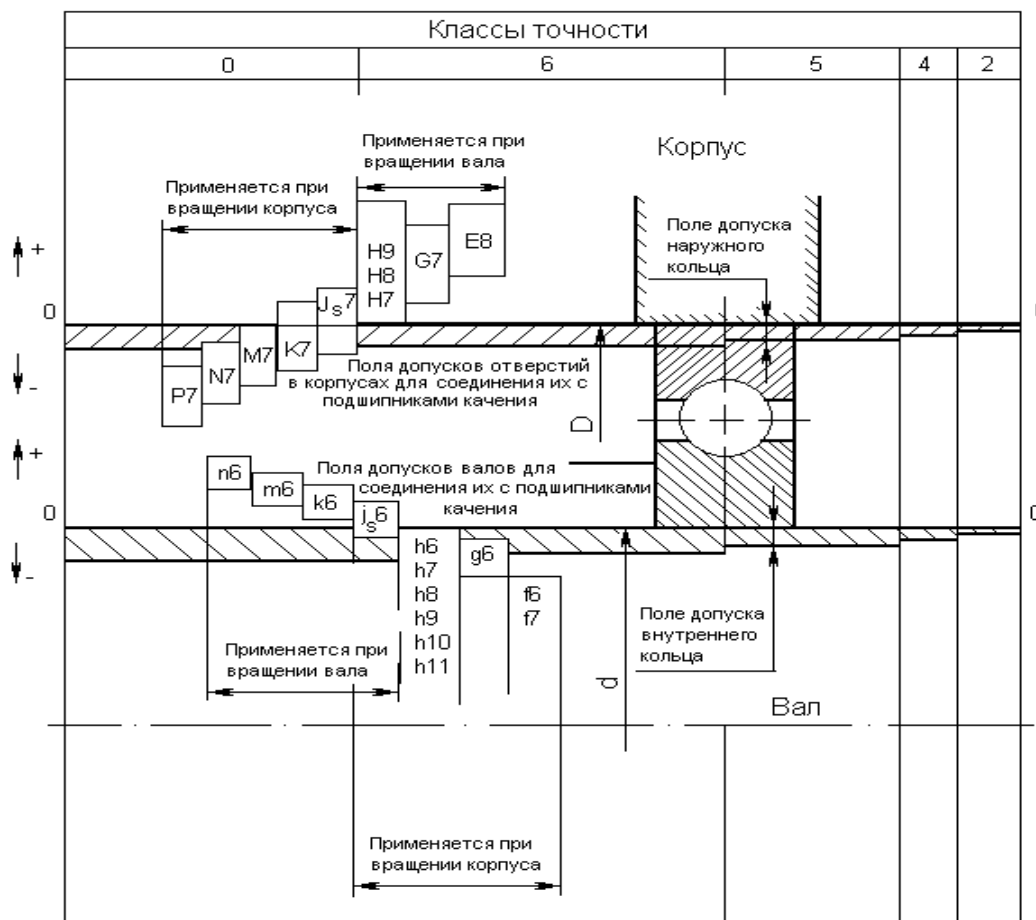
Схема расположения полей допусков на присоединительные размеры подшипников, вала и корпуса
